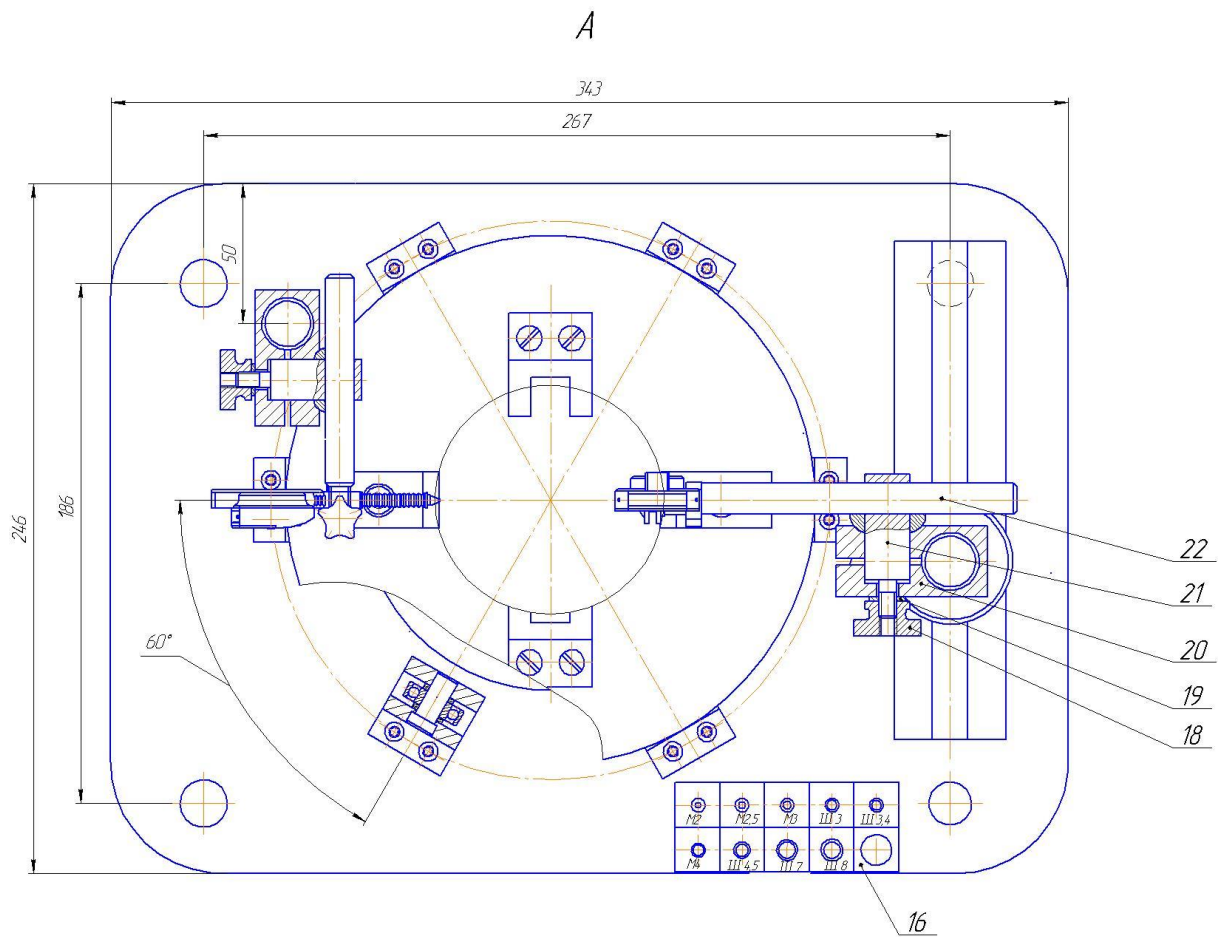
Эскиз контрольного приспособления (вид с верху)
